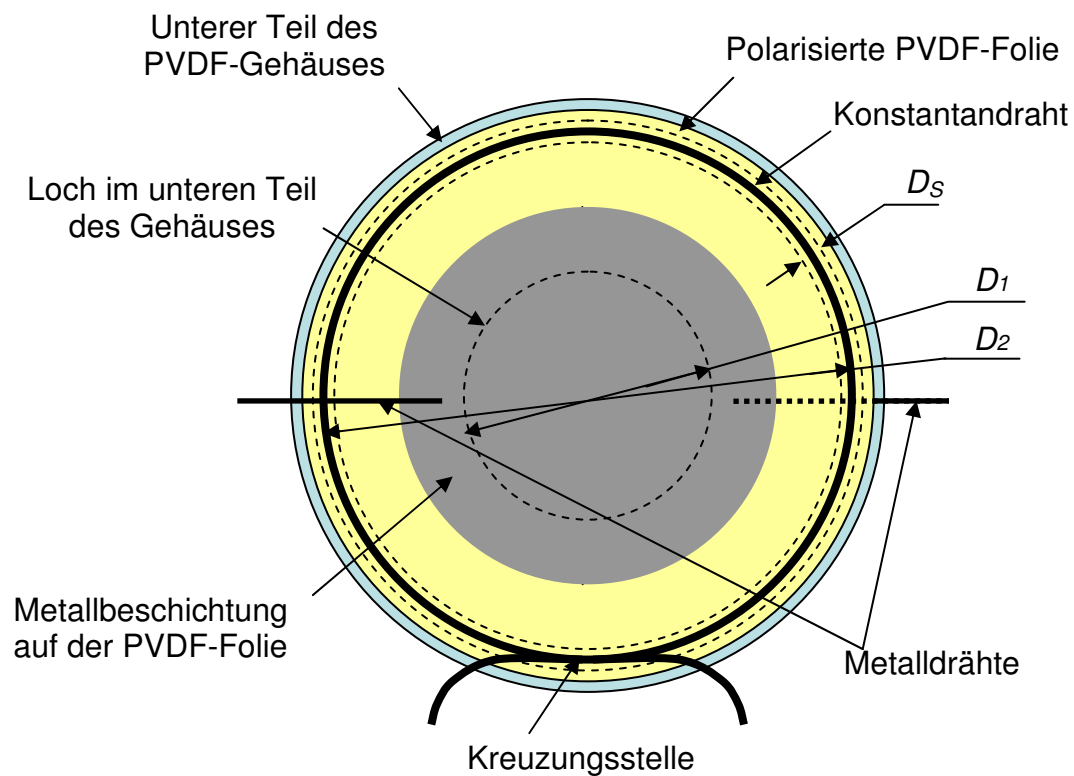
Ansicht von oben auf einen PVDF-Druckwächter ohne oberes Gehäuseteil.
